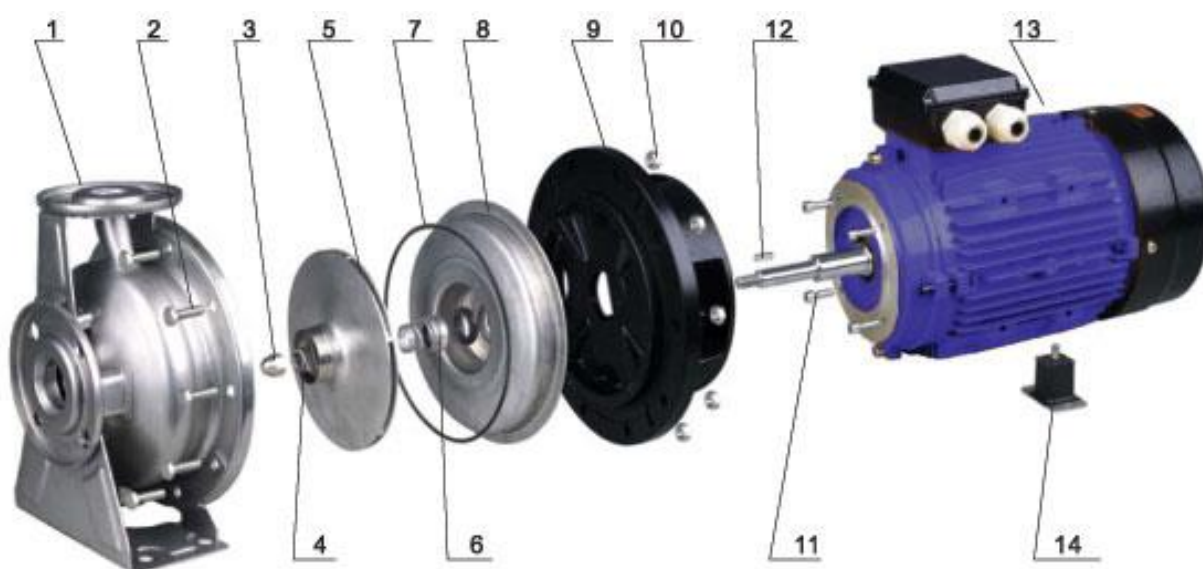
Типовая конструкция центробежного насоса (тип КМ): 1 – корпус насоса; 2 – крепежный болт; 3 – гайка-обтекатель РК; 4 – пружинная шайба; 5 – рабочее колесо; 6 – торцовое уплотнение; 7 – уплотнительное кольцо; 8 – крышка насоса; 9 – карданный шарнир; 10 – крепежная гайка; болт крепежный ЭД; 12 – шпонка; 13 – электродвигатель; 14 – лапа основания.
